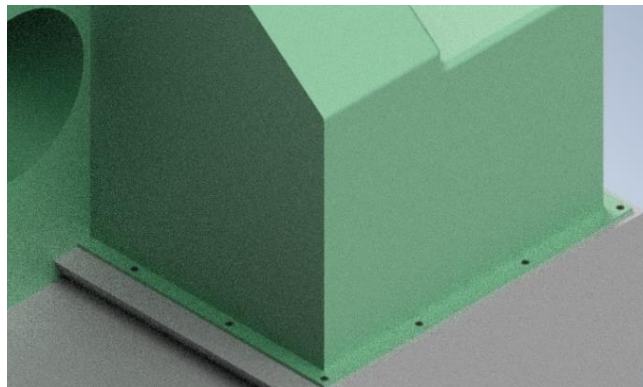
Anclaje tapa del motor y ejes motrices (1)
